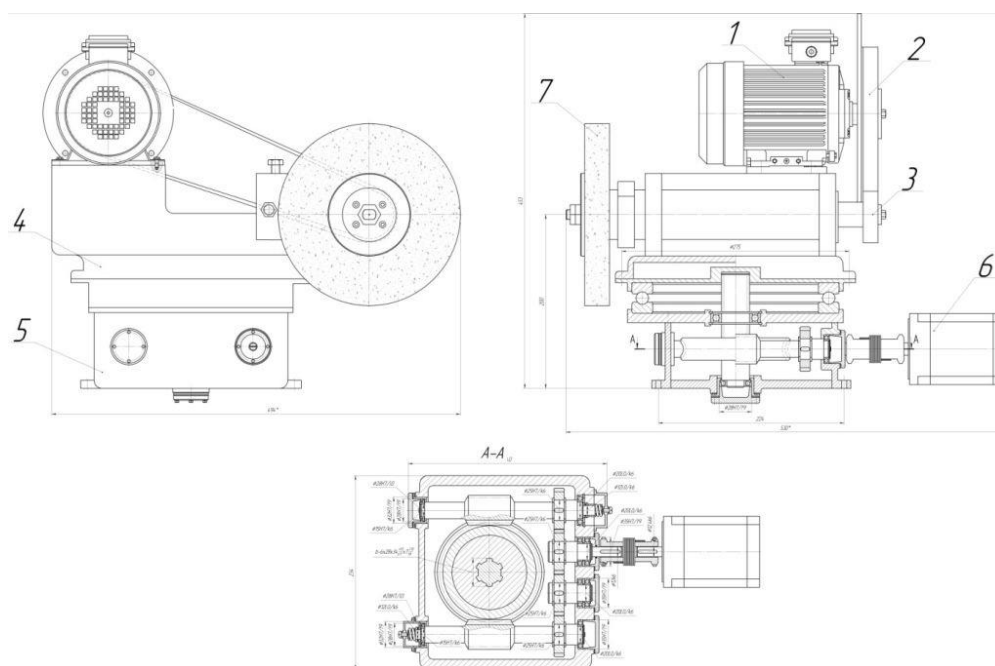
Конструкция модернизированной шлифовальной бабки и поворотного устройства (1 – двигатель привода круга, 2 – ременная передача, 3 – шпиндельный узел, 4 – корпус, 5 – поворотное устройство, 6 – шаговый двигатель привода поворотного устройства, 7 – шлифовальный круг)
